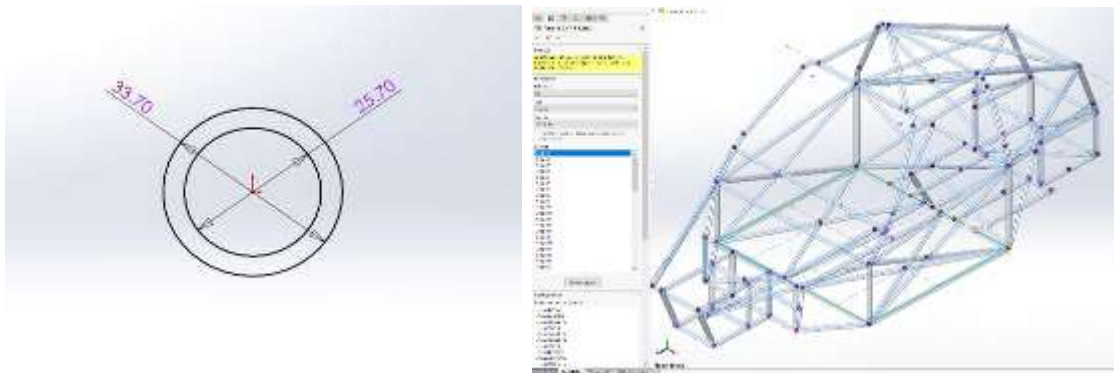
a) Geometría del miembro estructural b) Grupos del miembro estructural
